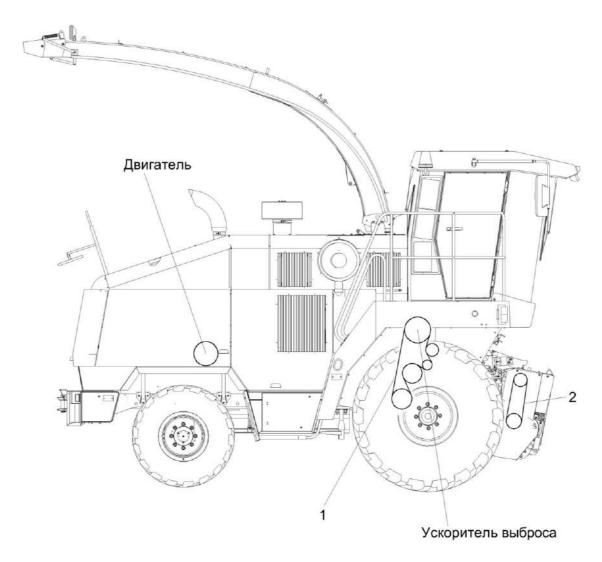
Схема приводов измельчителя (вид справа)
